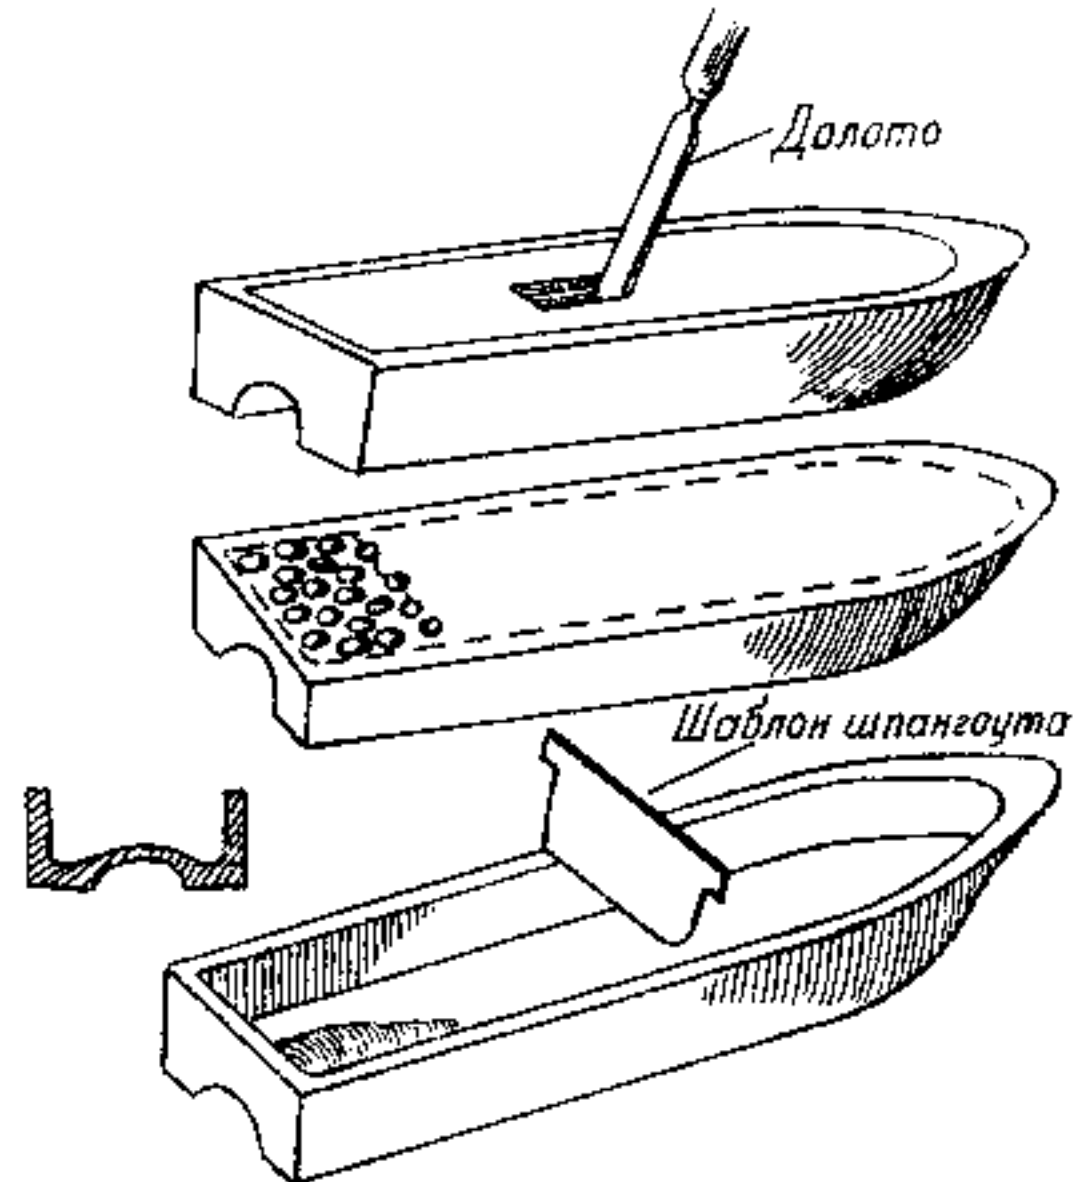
Видовбування й висвердлювання корпусу; замірювання шаблоном шпангоута.
